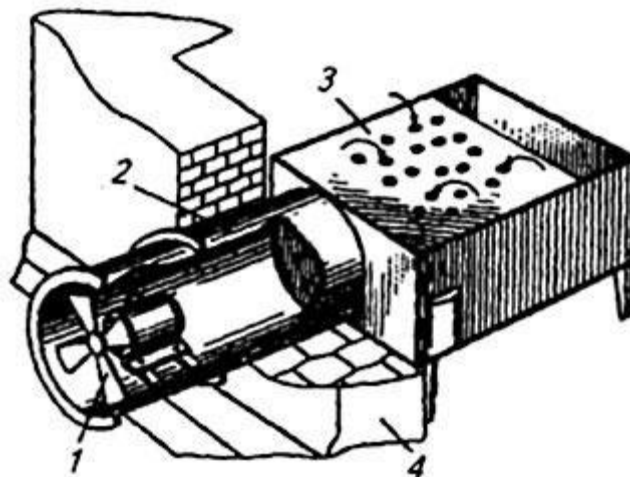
Конструкція витяжної вентиляційної системи на робочому місці зварювальника: 1 – вентилятор; 2 – витяжна труба; 3 – стіл зварювальника; 4 – частина стіни ремонтної майстерні
